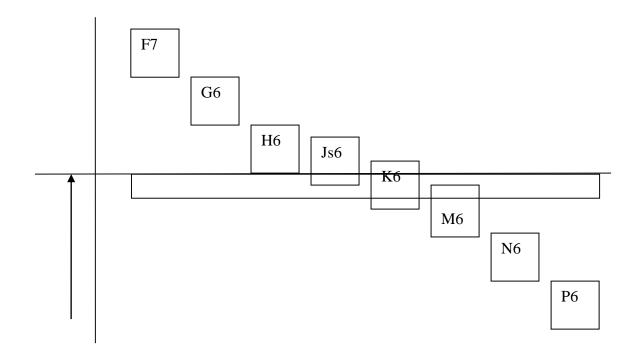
Эскизы деталей и сопряжения для посадки с полем допуска h5 в системе вала
